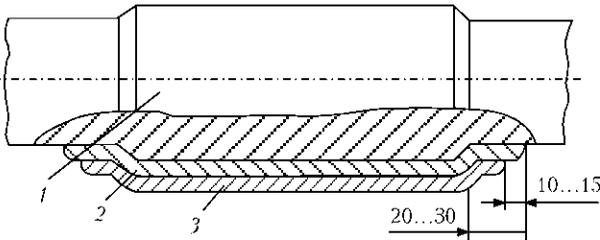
Схема выполнения антикоррозионной наплавки вала: 1 — основной металл; 2 — низкоуглеродистый металл наплавленного подслоя; 3 — высоколегированный аустенитный наплавленный металл
